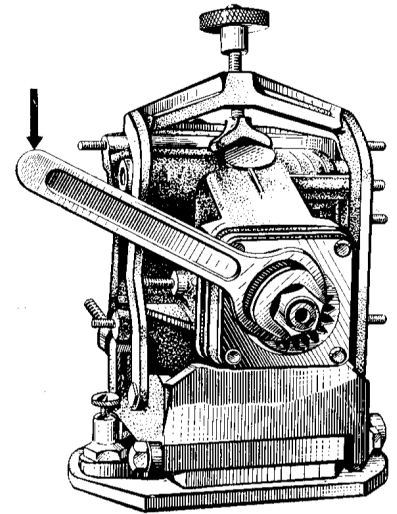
Стопореие стопором зубчатого фланца редуктора заднего моста от проворачивания и отвертывание гайки
